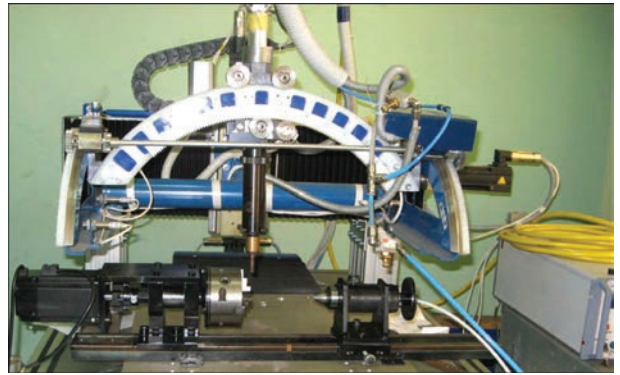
Технологический комплекс для лазерной сварки сильфонных компенсаторов
